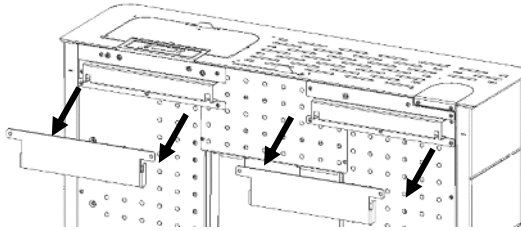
Colocación del equipo en los apoyos fijados en la pared
